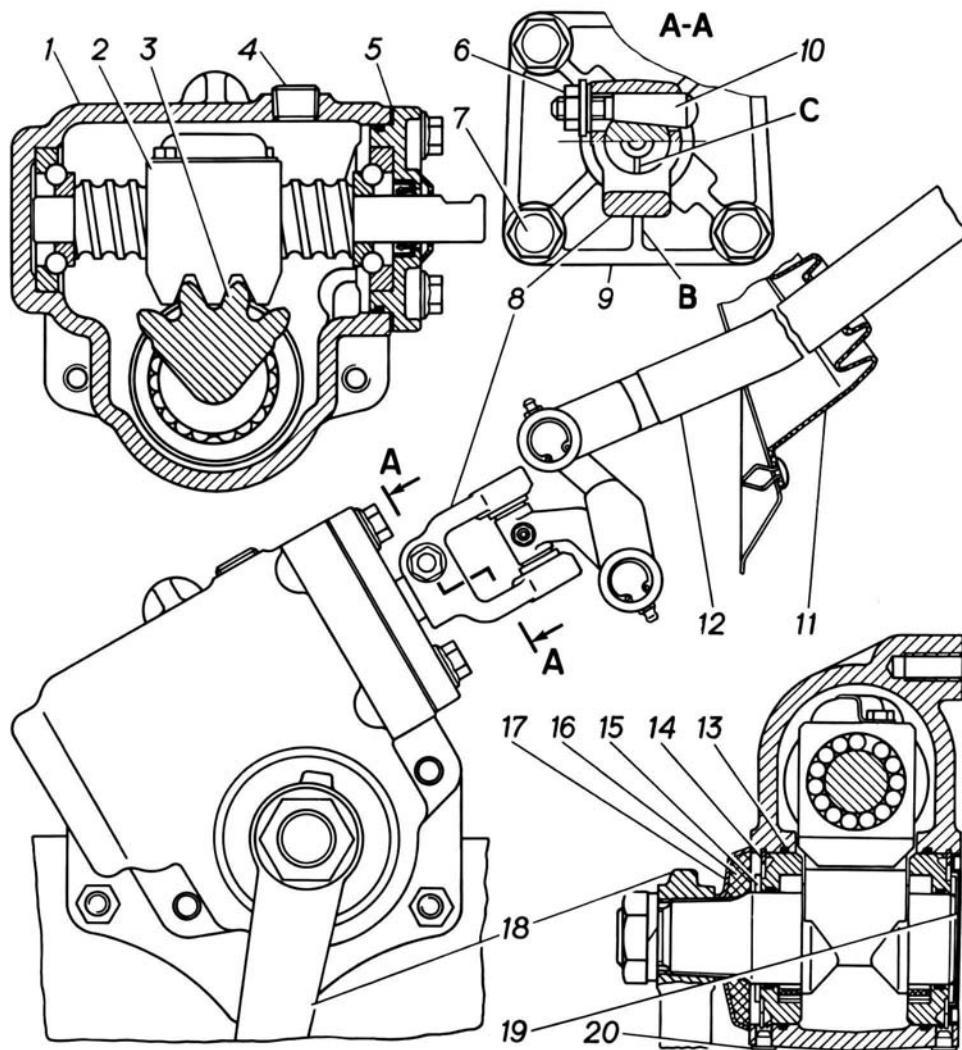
Рулевое управление без ГУР: В – ребро на верхней крышке; С – риска на торце винта; 1 – картер; 2 – винт с шариковой гайкой; 3 – вал-сектор; 4 – пробка заливного отверстия; 5 – регулировочные прокладки; 6 – гайка; 7 – болт; 8 – вилка; 9 – крышка; 10 – клин; 11 – уплотнитель рулевого вала; 12 – карданный вал; 13 – уплотнительное кольцо; 14 – стопорное кольцо; 15 – наружное кольцо подшипника вала-сектора; 16 – уплотнитель вала-сектора; 17 – крышка; 18 – сошка; 19 – боковая крышка; 20 – пробка
